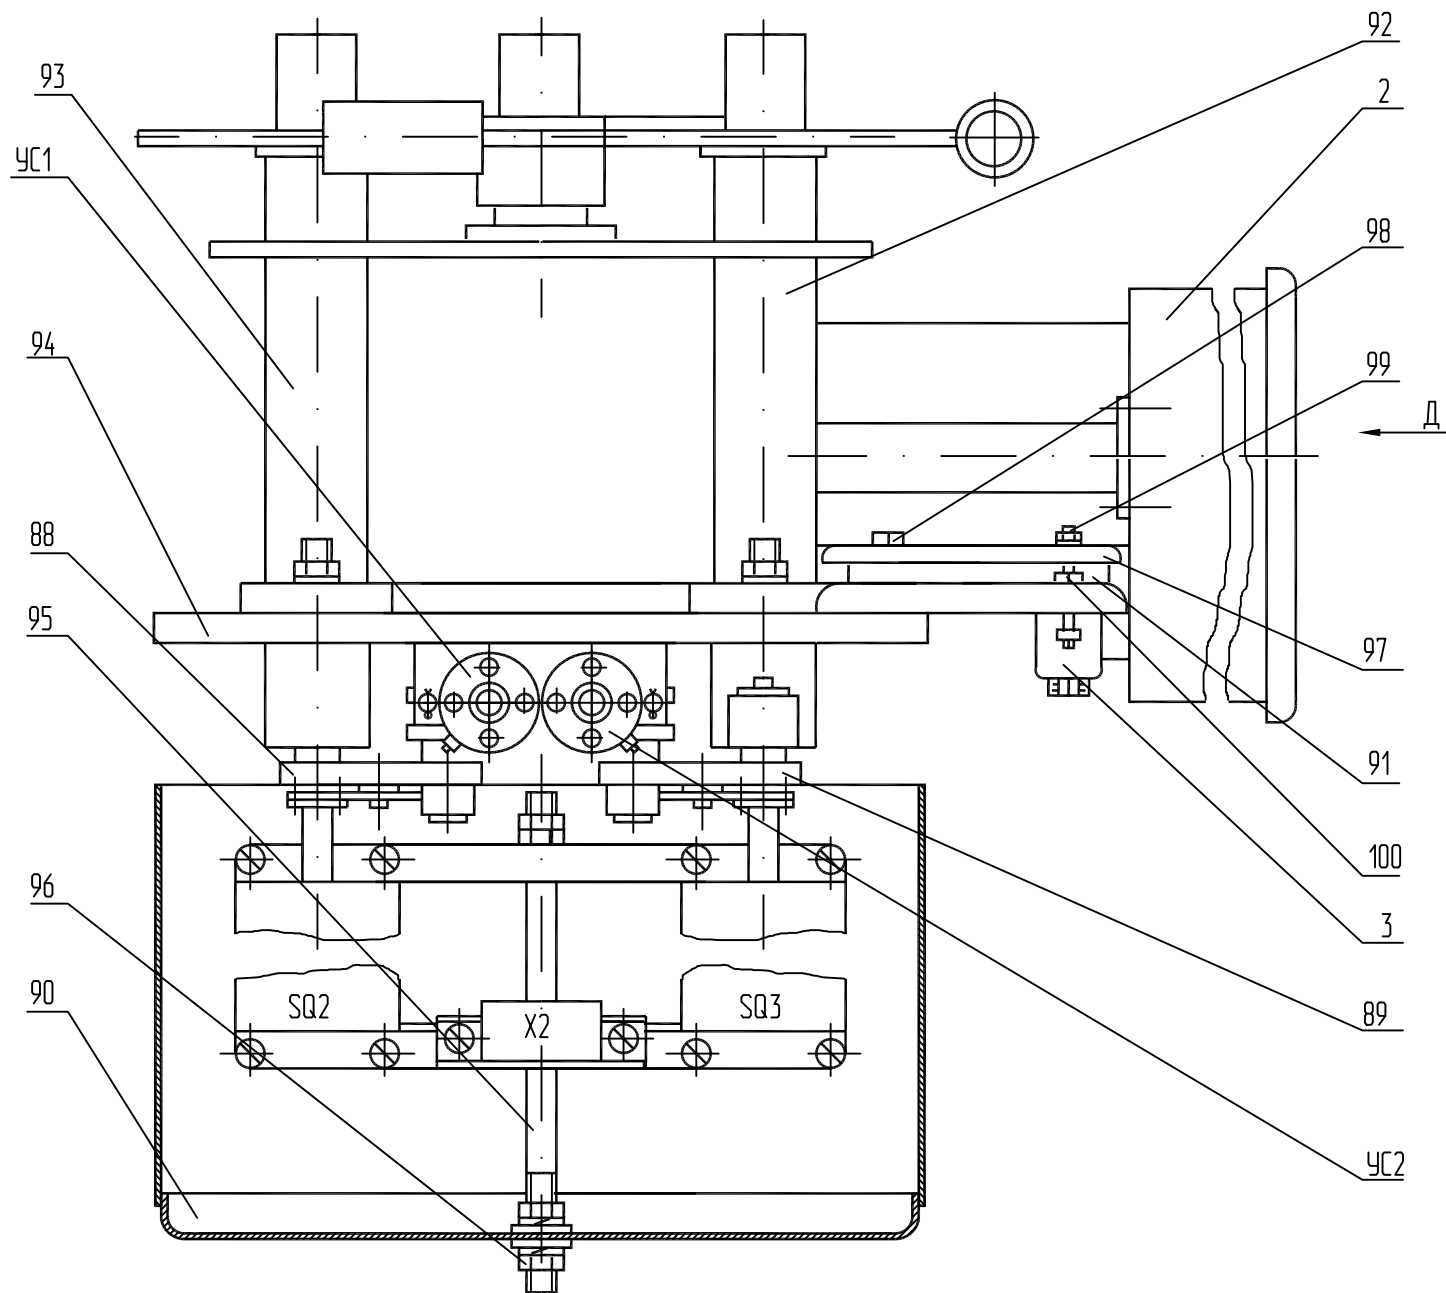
Установка механизма редуктора для поворота выходного вала привода на угол 270°
